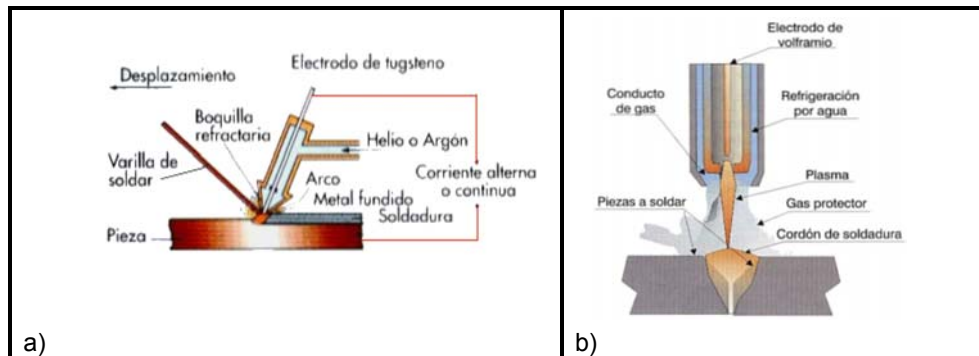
Soldadura Con electrodo refractario (método TIG). Tecnología industrial. I.E.S. “Cristóbal de Monroy”. Dpto. de Tecnología.
